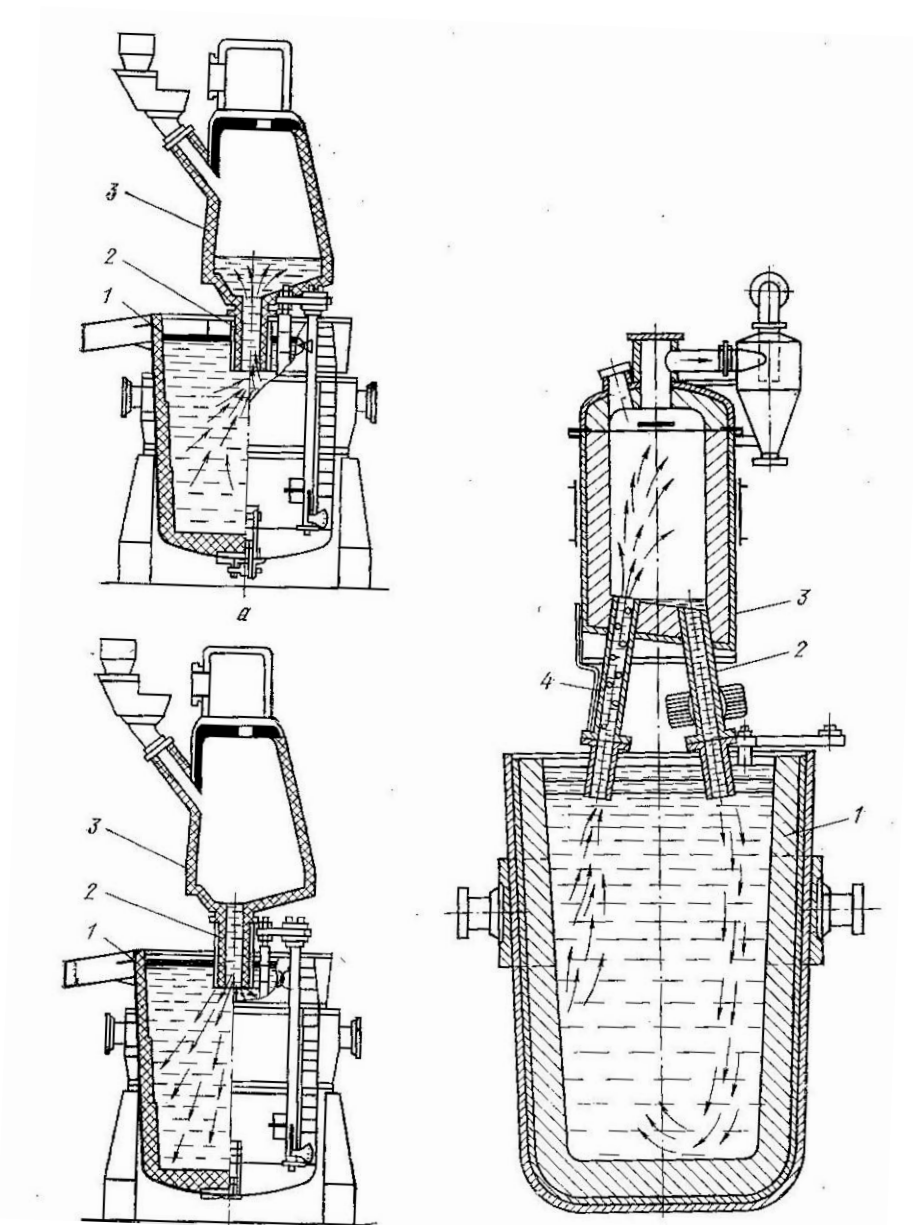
Схема порционного и циркуляционного вакуумирования стали: 1 — сталеразливочный ковш; 2 — патрубок; 3 — вакуум-камера; 4 — всасывающий патрубок
